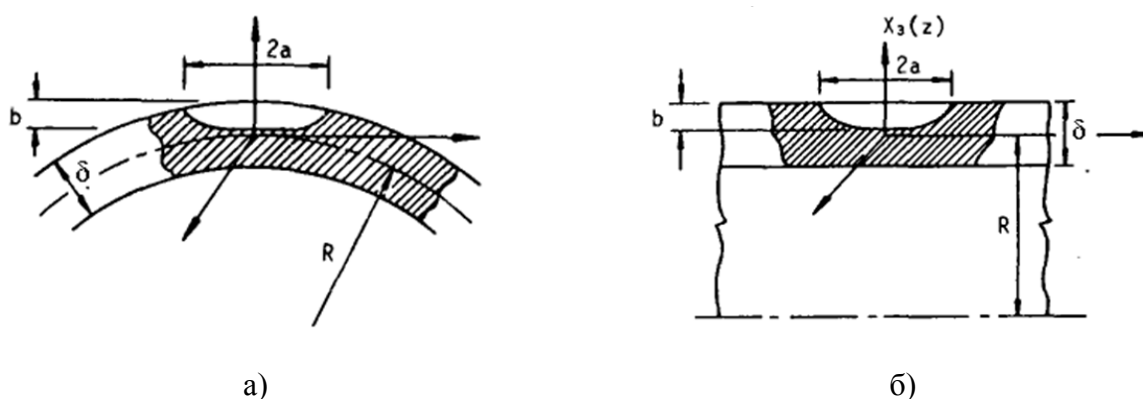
Положение трещин на внешней поверхности корпуса РДТТ:
